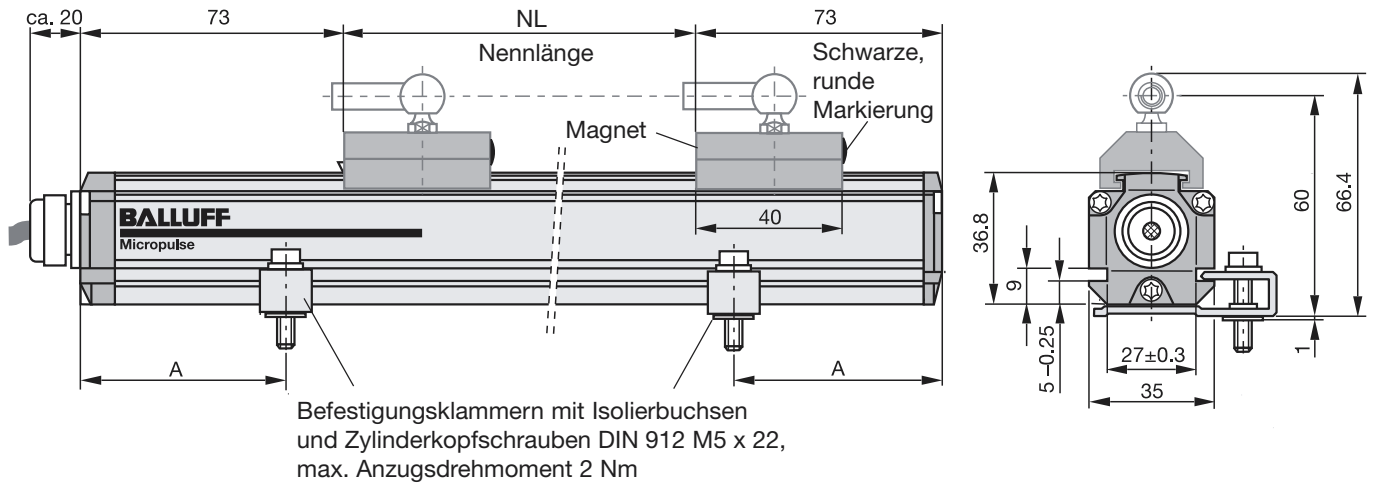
Maßzeichnung (Wegaufnehmer BTL5...P-KA.. mit geführtem Positionsgeber BTL5-F-2814-1S)
